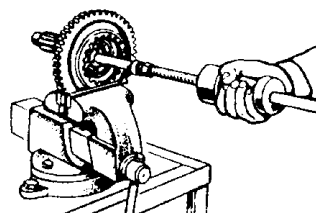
Выпрессовка подшипника № 208 из вторичного вала.
